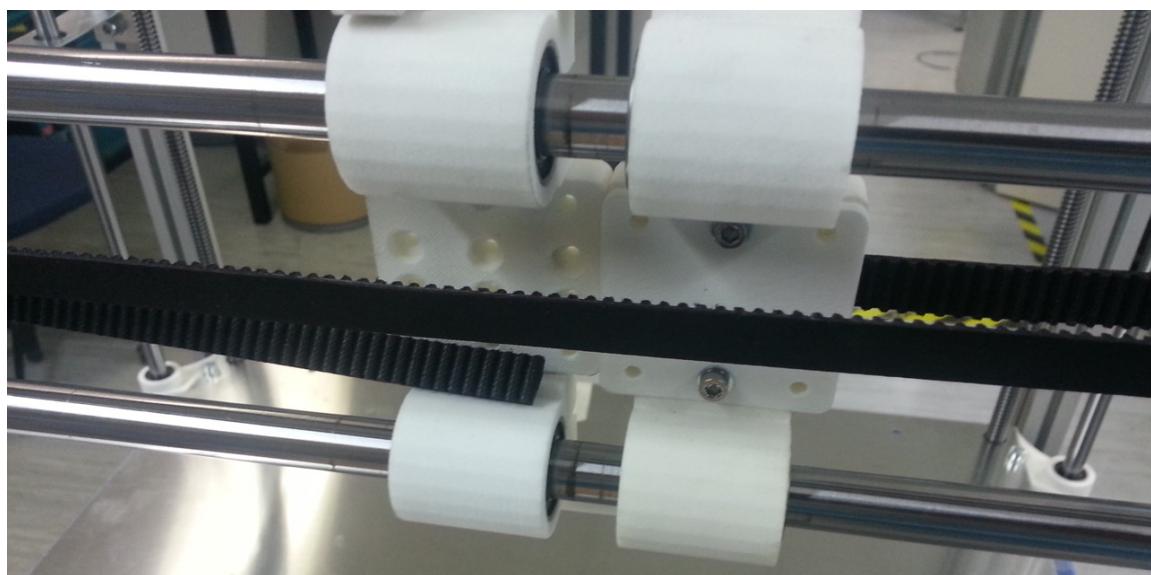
Finish timing belt X-axis front side (Dual-Extruder)
